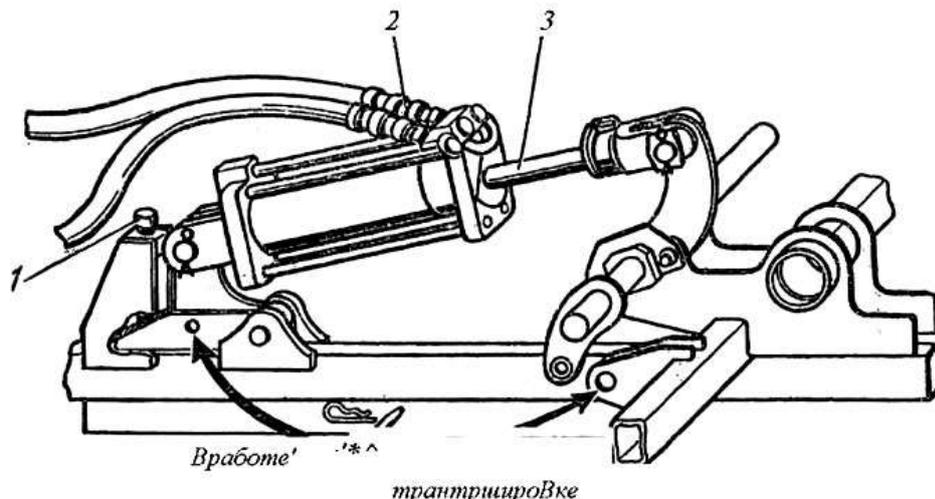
Устройство для подъема и регулировки глубины хода сошников сеялки СЗ-3,6:
